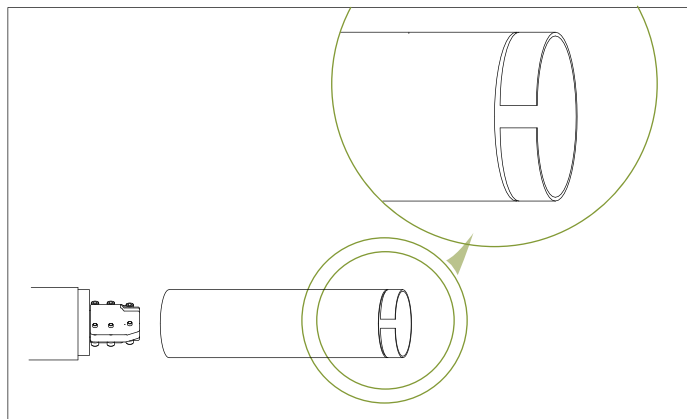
Установка патрубков, концы с пазом направлены наружу
